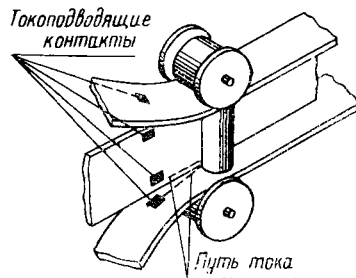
Схема непрерывного процесса изготовления балки из трех полос с помощью ВЧ сварки
